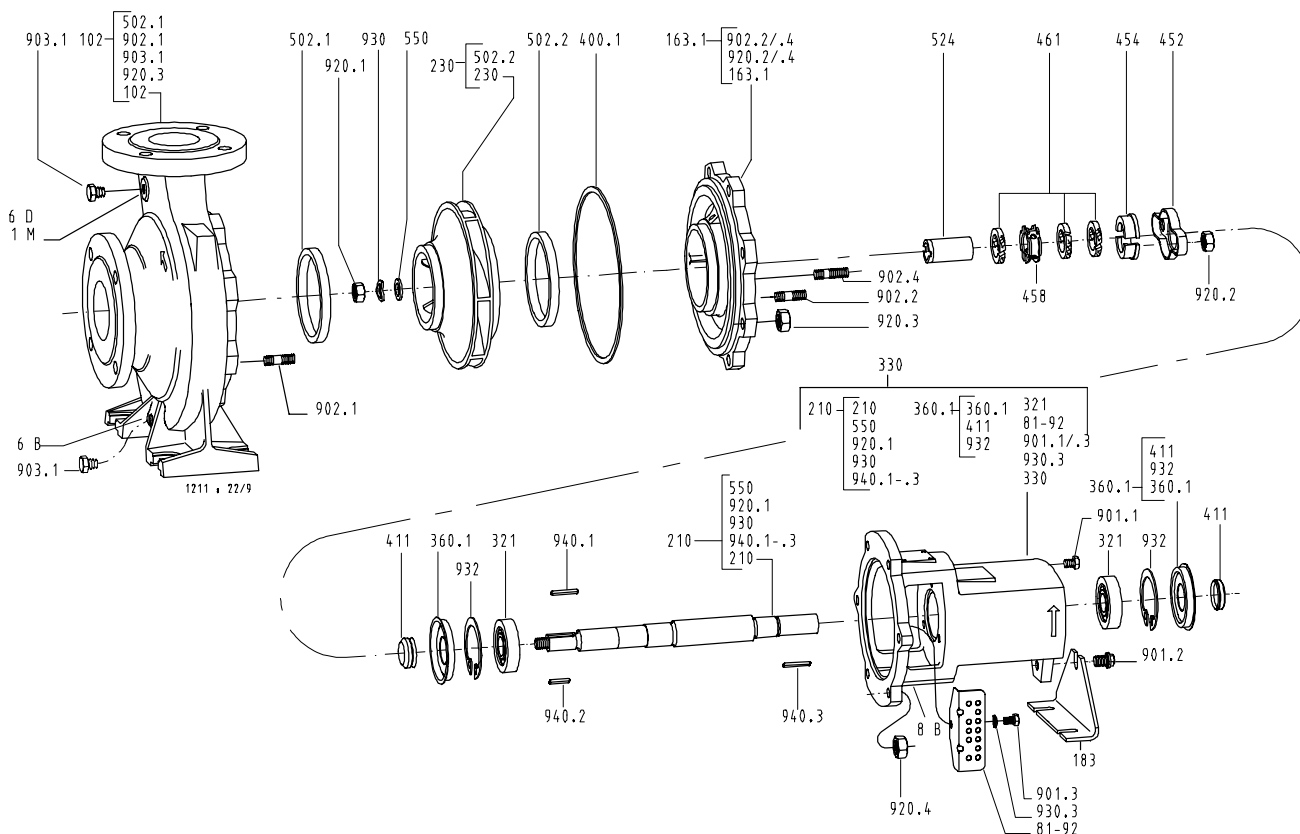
Сальниковая набивка и резьбовая крышка корпуса
